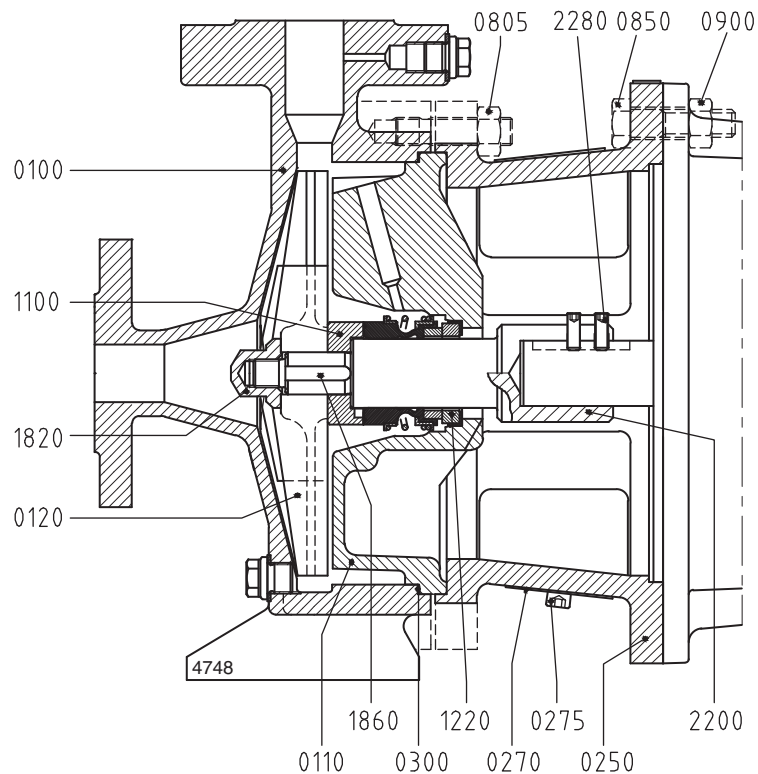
Assemblage de l'arbre de liaison pour pompes de taille 25-...
